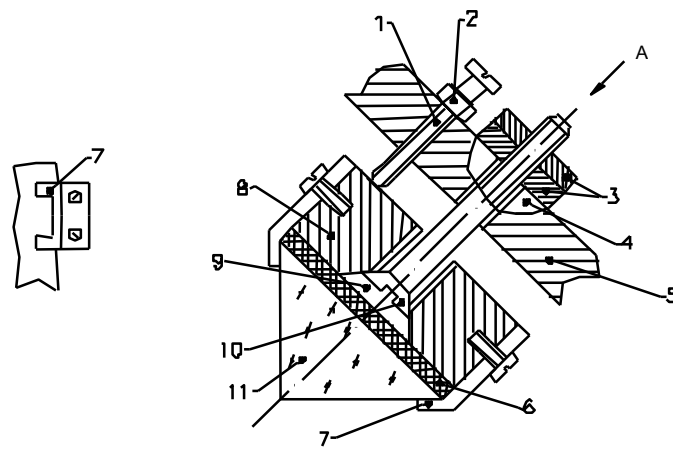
Кріплення призми АР-90⁰, що юстується: 1 – упорний гвинт, що відштовхує основу з призмою від корпусу приладу; 2 – гайка, що стопорить гвинт; 3 – гайка, що притягає гвинт до корпусу; 4 – кульковий шарнір, у якому призма може качатися по двох координатах; 5 – корпус приладу; 6 – прокладка; 7 – лапка; 8 – основа; 9 – конічний отвір під гвинт-вісь; 10 – потайний гвинт-вісь з конічною голівкою, що притягає основа (призми до корпусу приладу); 11 – призма
